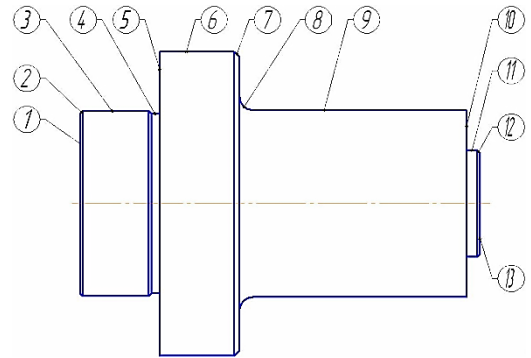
Число оброблюваних поверхонь деталі типу «Вал».
